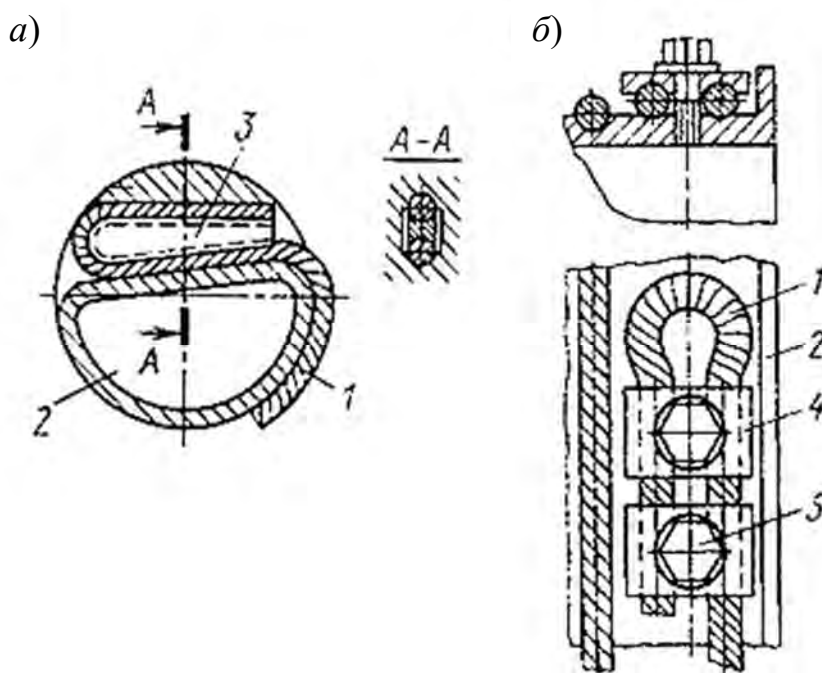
Крепления каната к барабану: 1 – канат; 2 – барабан; 3 – клин; 4 – планка; 5 – болт
